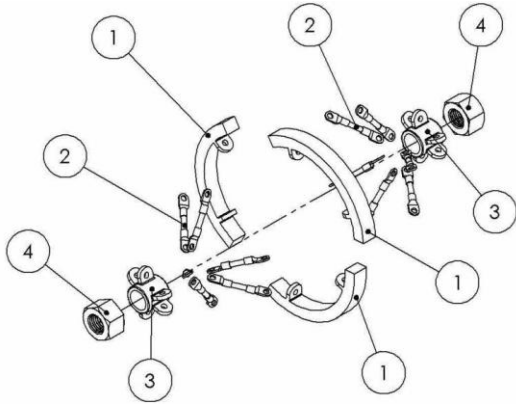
Vista explosionada del sistema de respaldo para soldaduras circunferenciales.
